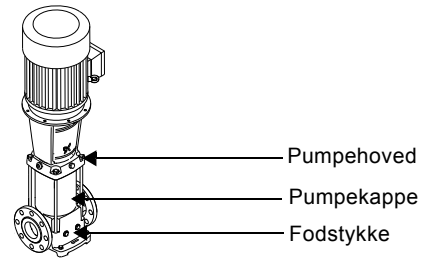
Varme eller kolde overflader på en CR-, CRI-, CRN-pumpe
